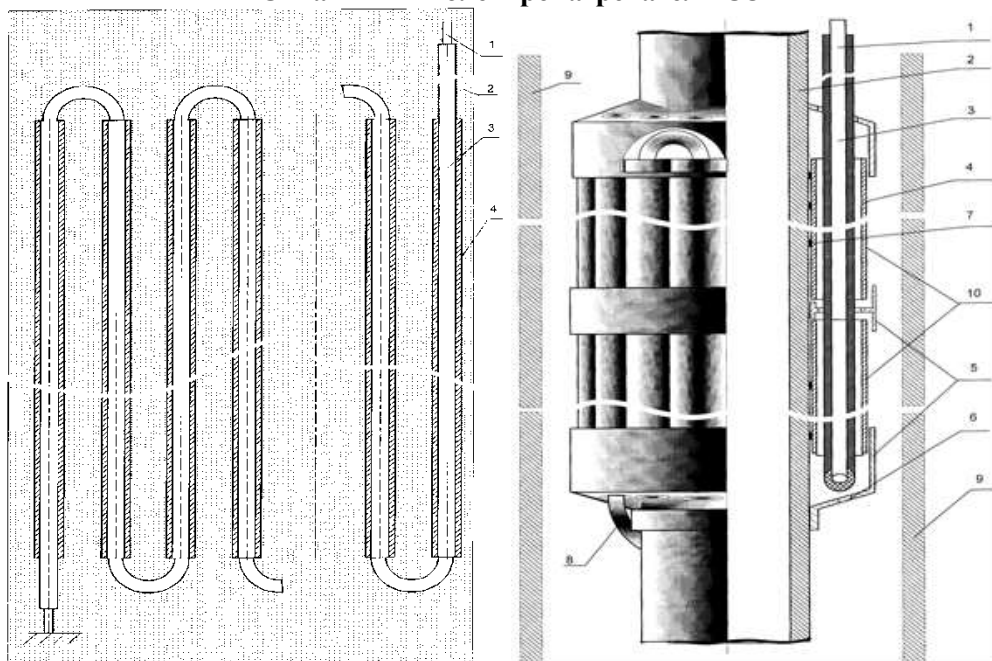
Скважинный электронагреватель СЭНАМ и развертка его нагревательных элементов
